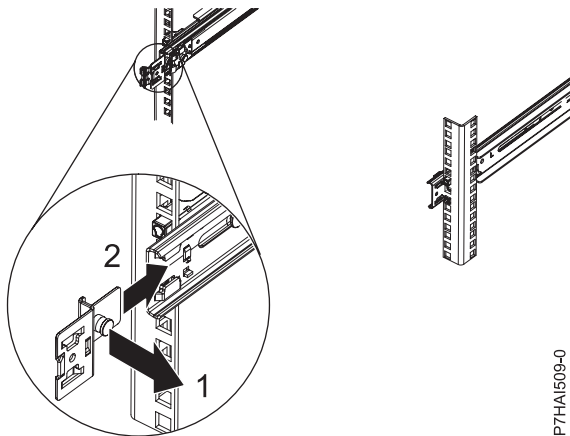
Вытянутый штырь крепежной скобы и крепежная скоба, установленная в направляющей
